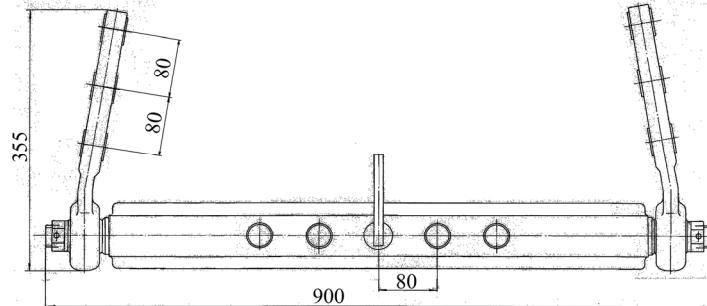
Схема установки ТСУ-1Ж-01
